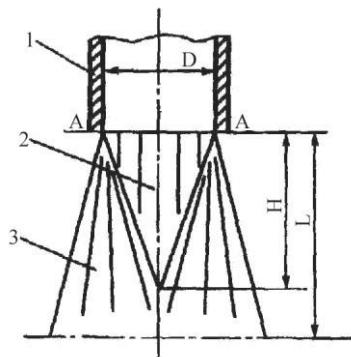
Схема газового потока из сопла сварочной горелки:
